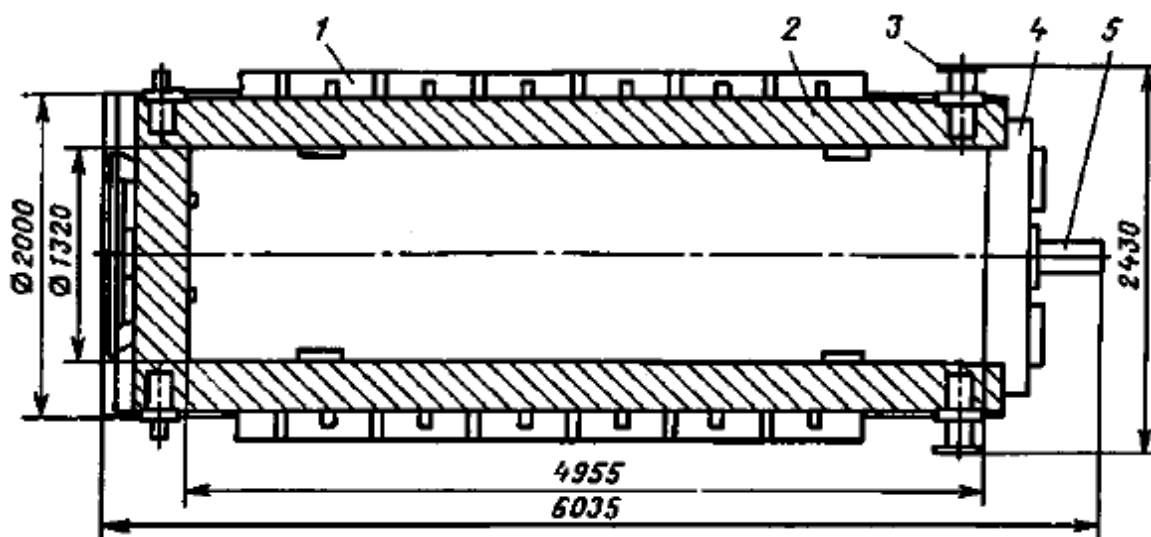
Контейнер ТК-13 для перевозки отработавших ТВС реактора ВВЭР-1000: 1 – нейтронная защита; 2 – корпус; 3 – цапфа; 4 – крышка; 5 – устройство под захват
